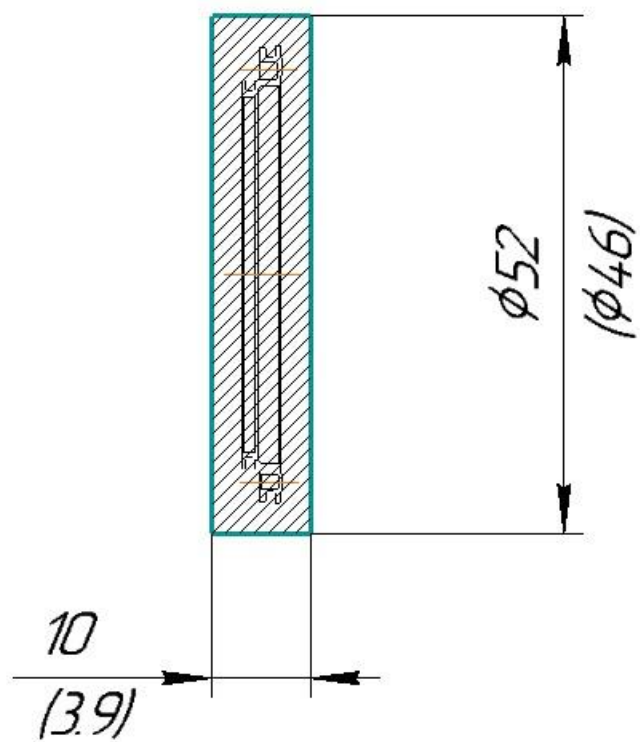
Ескіз заготовки з прокату (прутка)
